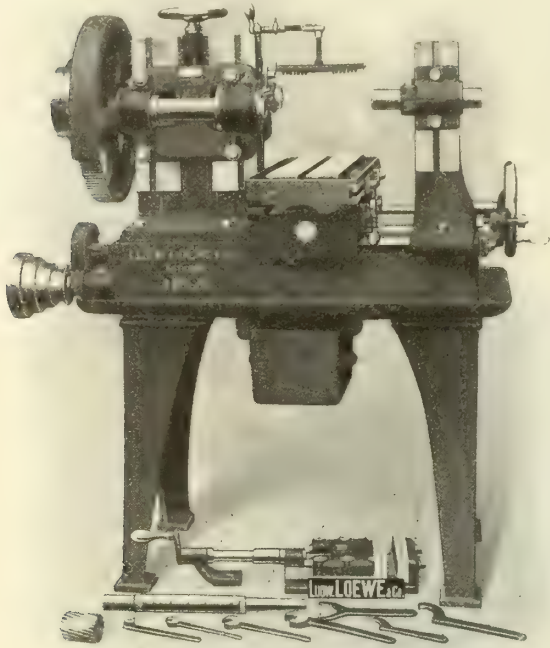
Selbsttätige Fräsmaschine mit verstellbarer Arbeitsspindel
